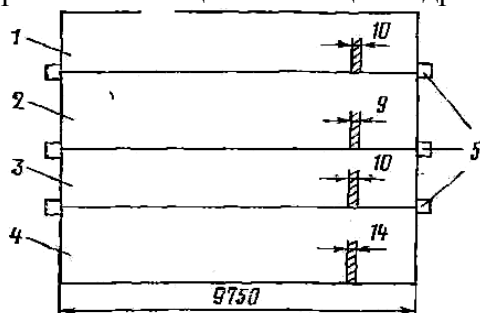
Схема раскладки листов цилиндрической части котла;
